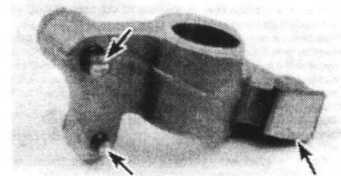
Отверните болты конструкции шатунового вала (указаны стрелками)
